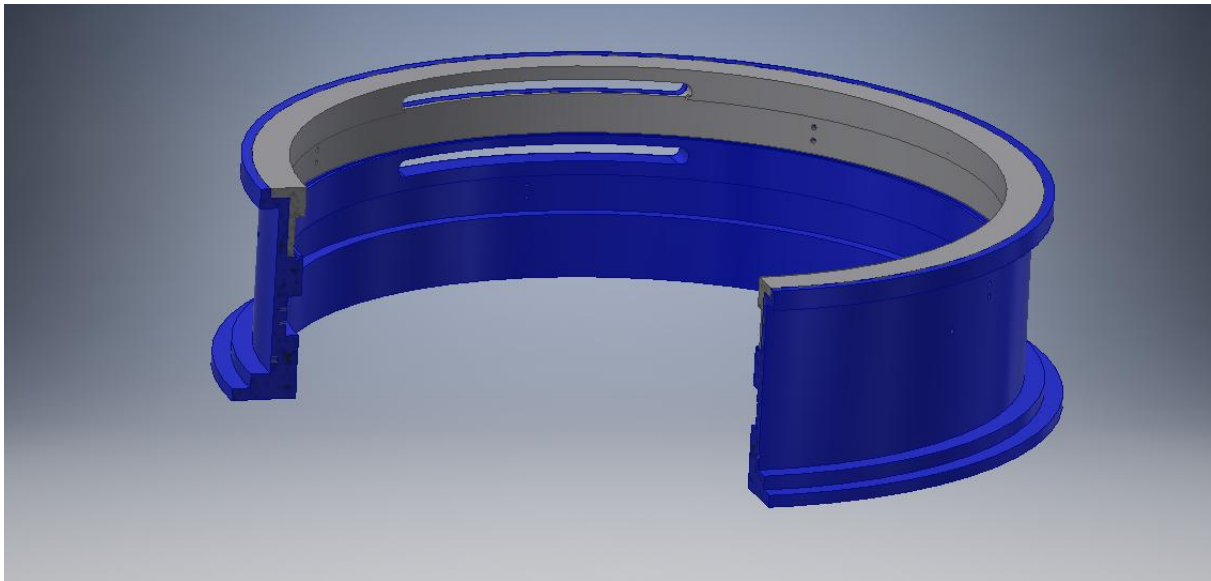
3D model - varianta č.2 v řezu
